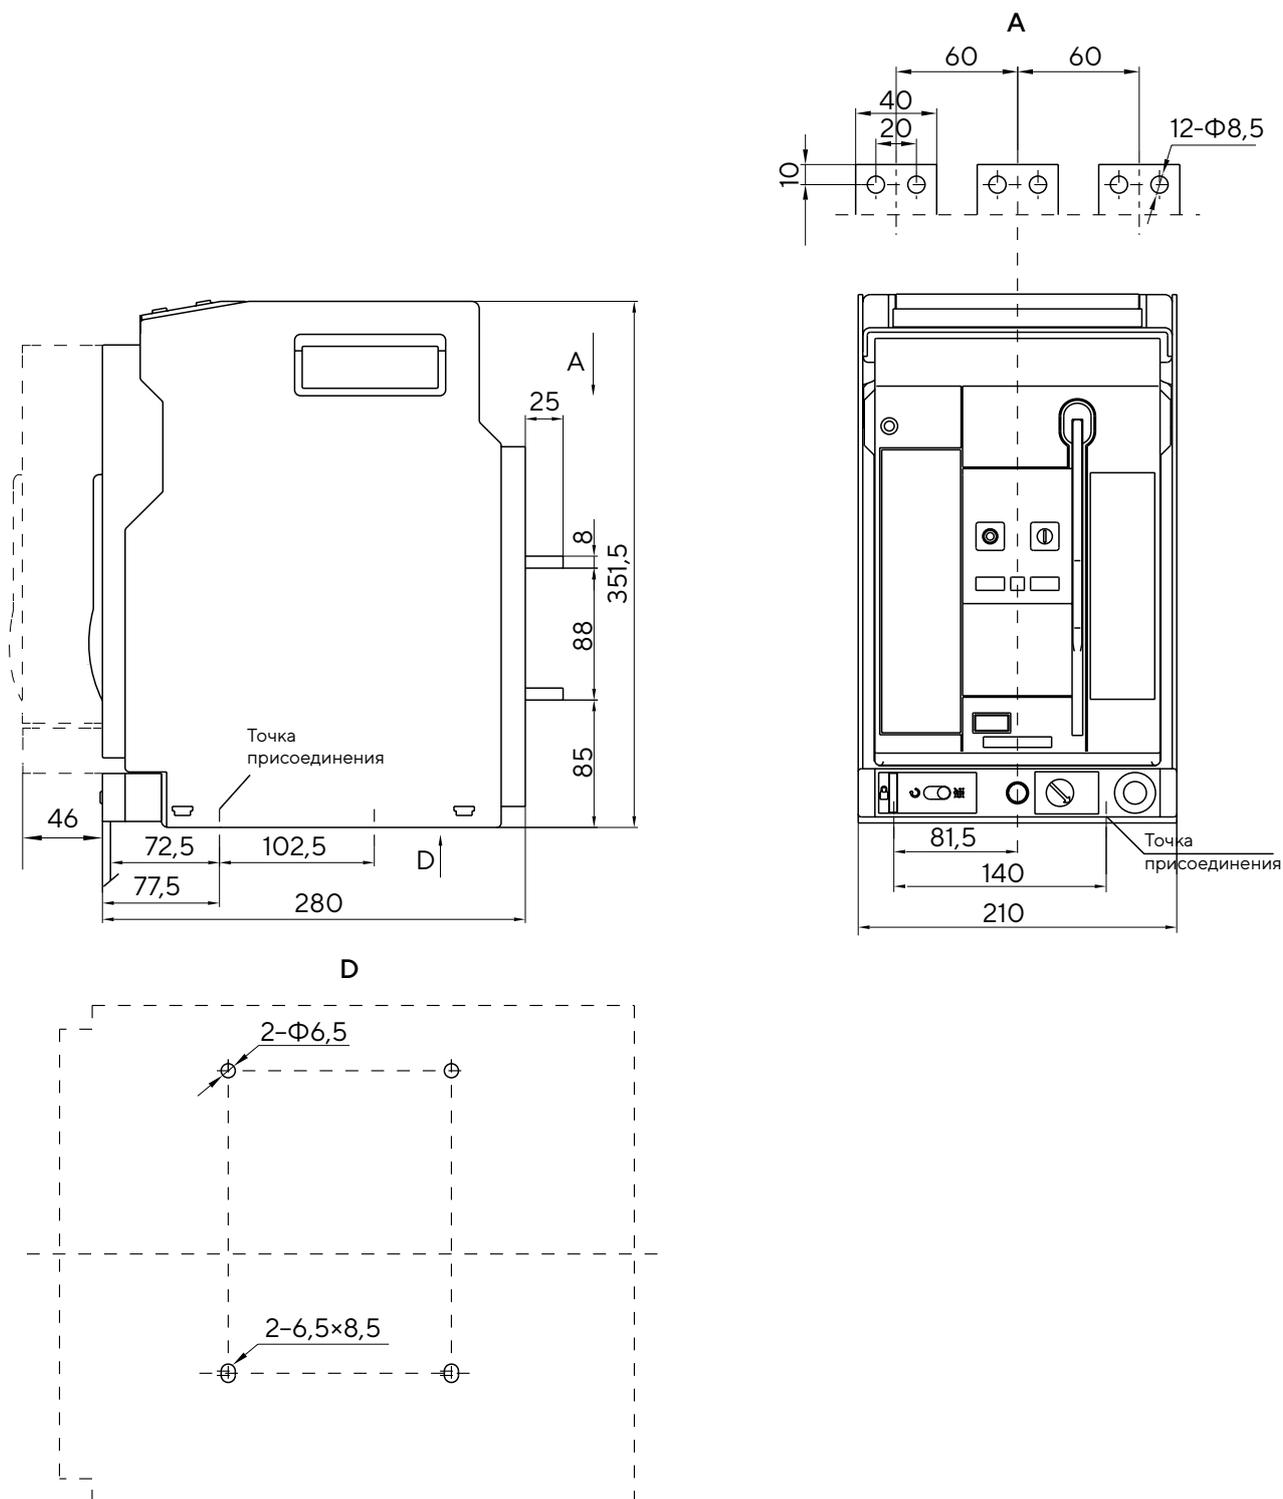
Габаритные размеры выдвижных трехполюсных выключателей типоразмера S
